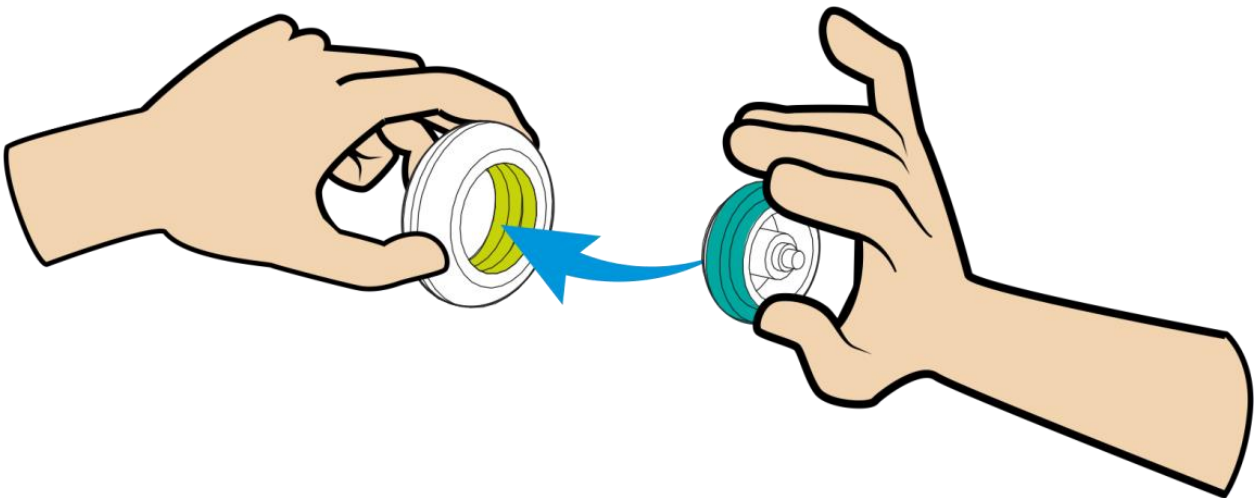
Ensamblaje 1.1.1 – 1.1.2
